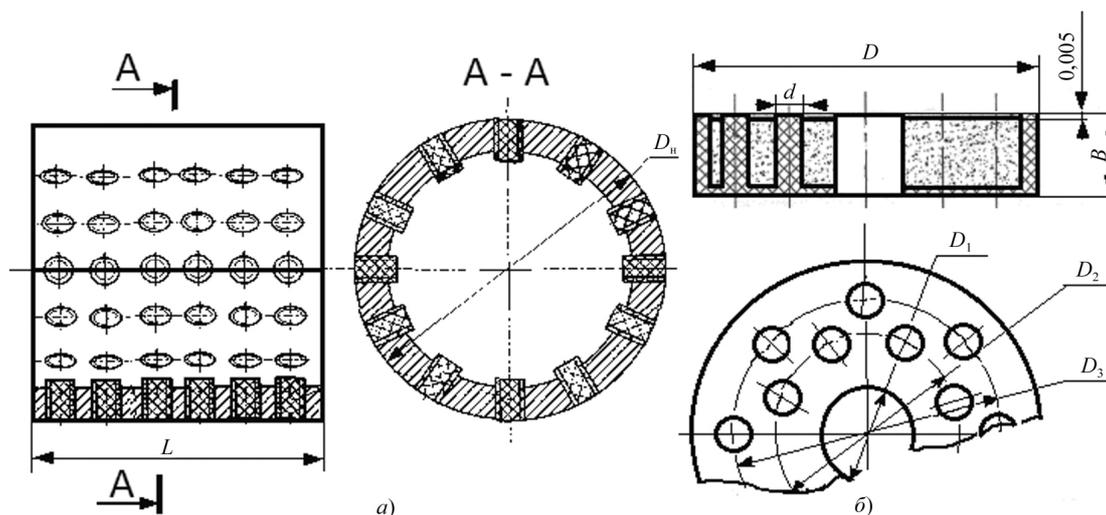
Полимерпорошковые подшипники: а – радиальный; б – упорный; D – диаметр подшипника; d – диаметр полимерной вставки; D_1 – диаметр резервуара для запасов смазки; D_2 , D_3 – диаметры кольцевых рядов вставок; D_n – наружный диаметр радиального подшипника; B – ширина подшипника
